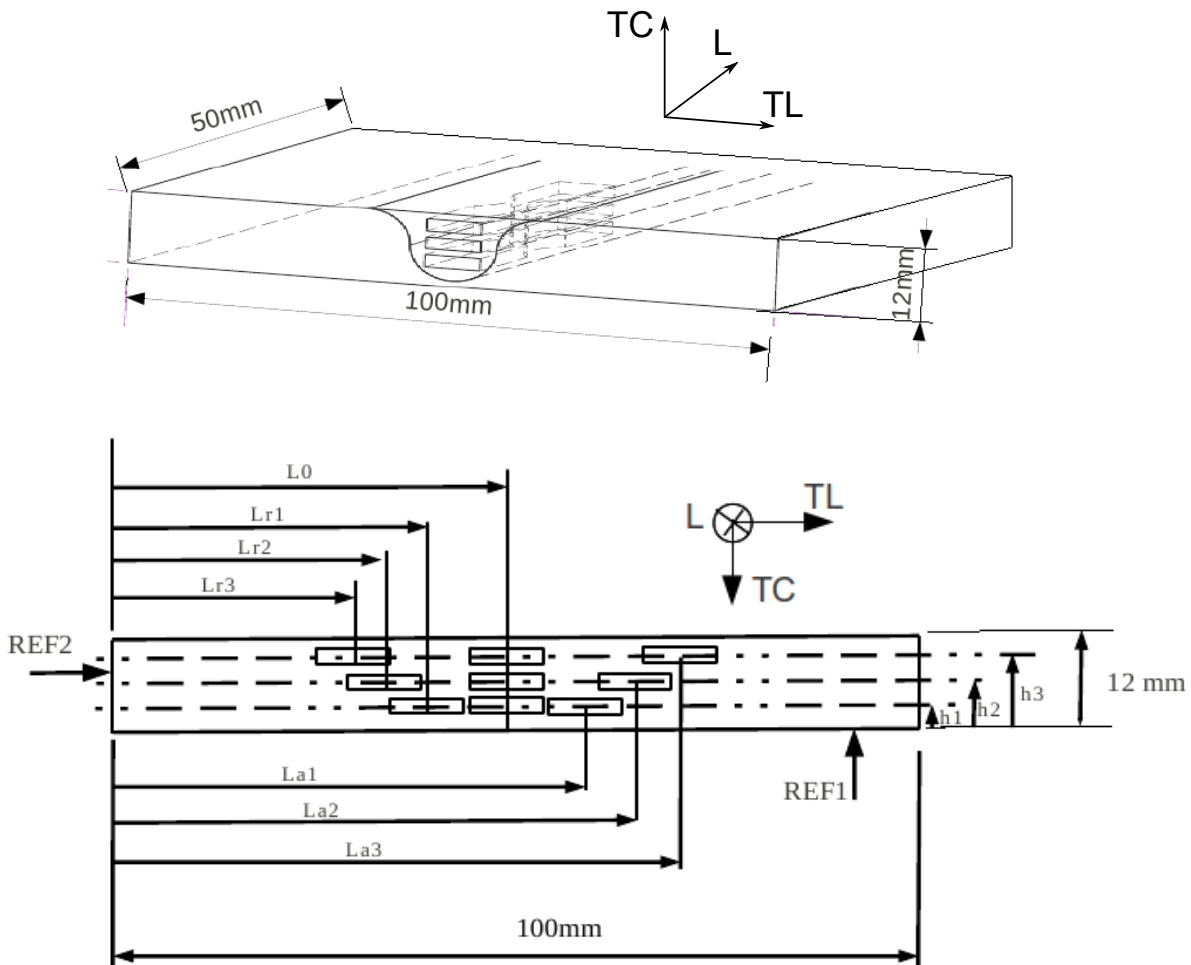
Définition des positions de prélèvement des mini-échantillons dans les joints soudés par FSW
